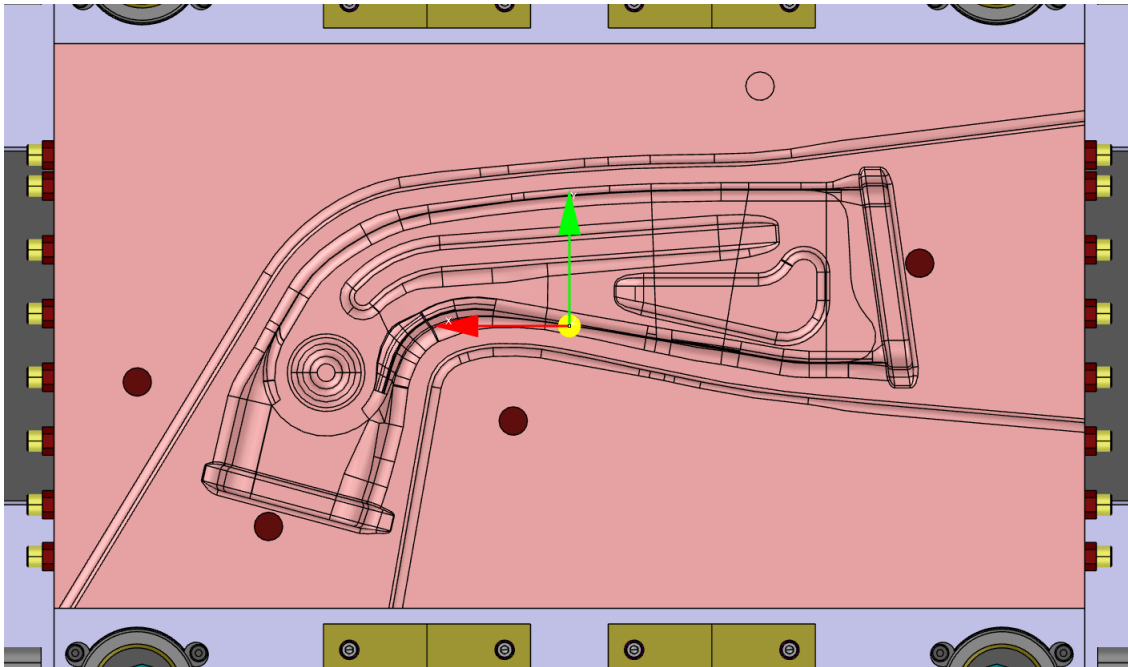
Demonstrator Werkzeug OT [Quelle: Schmidt Modellbau GmbH]
